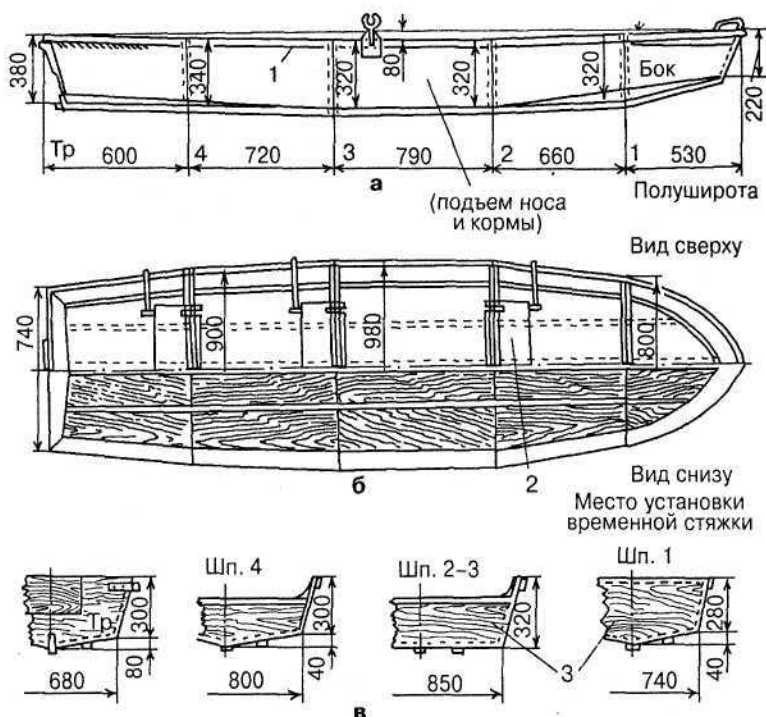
Основные размеры лодки (а), конструкция корпуса (б) и шпангоутов (в): 1 — трос; 2 — банка (650×270×10 фанера, 3 шт.); 3 — диафрагмы (фанера S=3)
